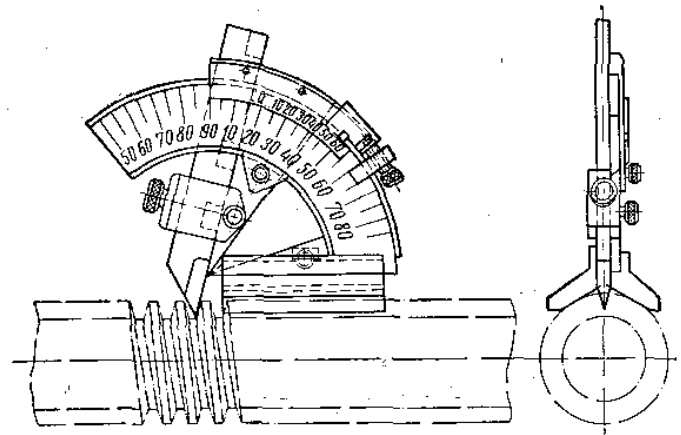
Угломер для измерения угла профиля трапецидальной резьбы
